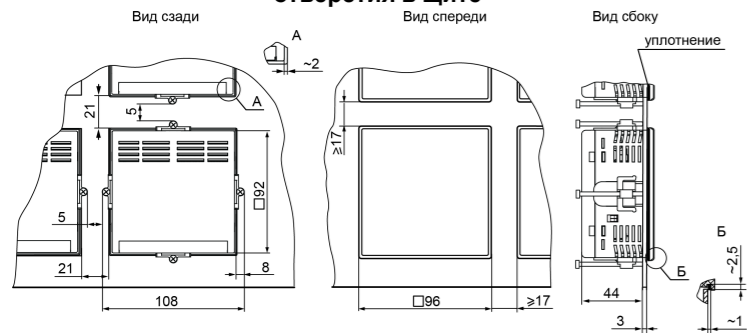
Корпус Щ1 в щите толщиной 3 мм
